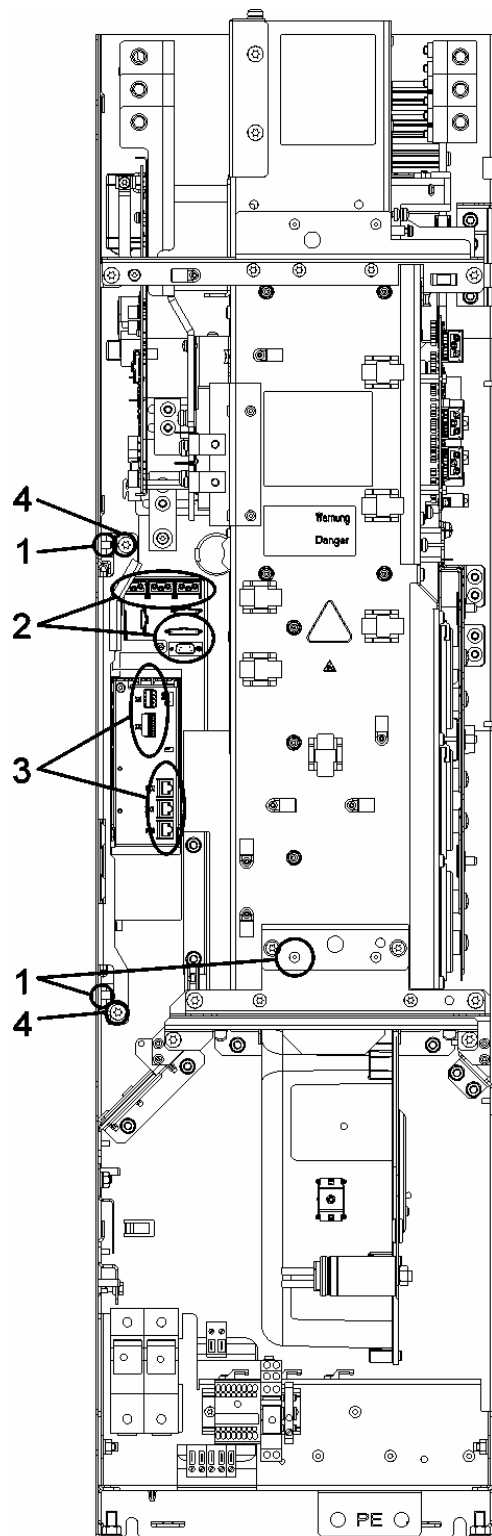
Замена платы Control Interface Board, типоразмер FX
